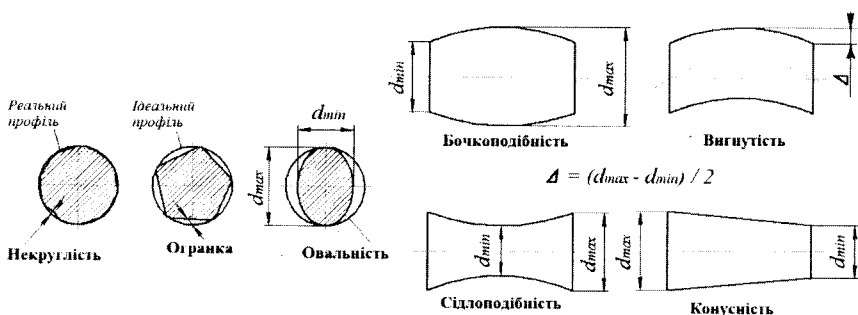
Відхилення форми деталей із циліндричними поверхнями
